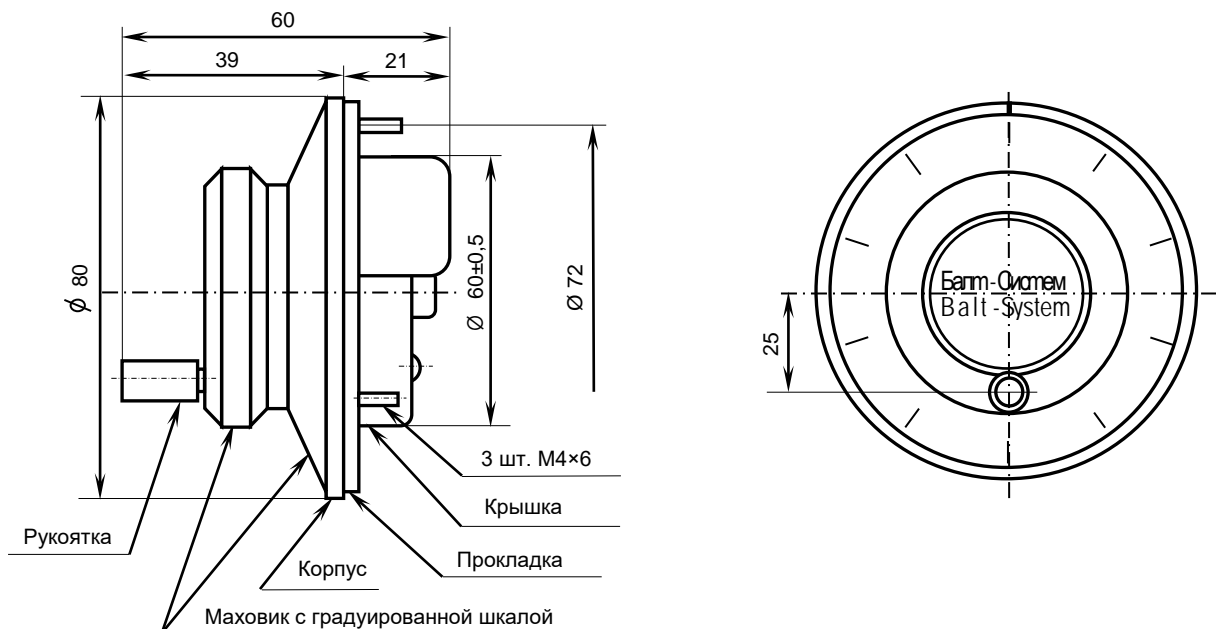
Габаритные размеры штурвала серии LGF
